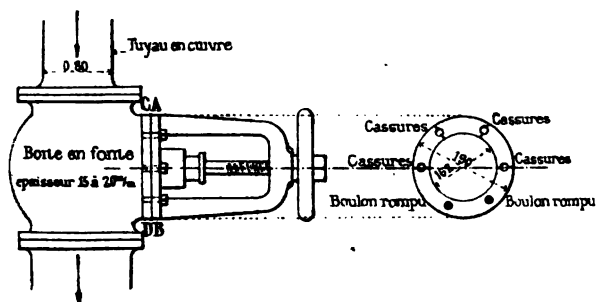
Détail de la valve (fig. 24) et indication des cassures de la bride CD.
